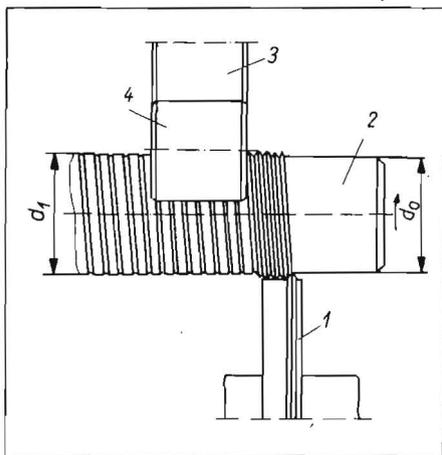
Wirkprinzip des Zweistufenkaltumformens;
